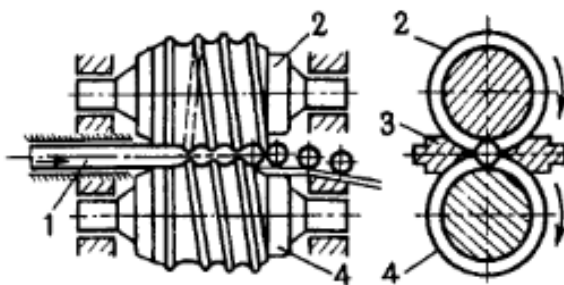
Схема прокатки шаров в стане поперечно-винтовой прокатки [2]
